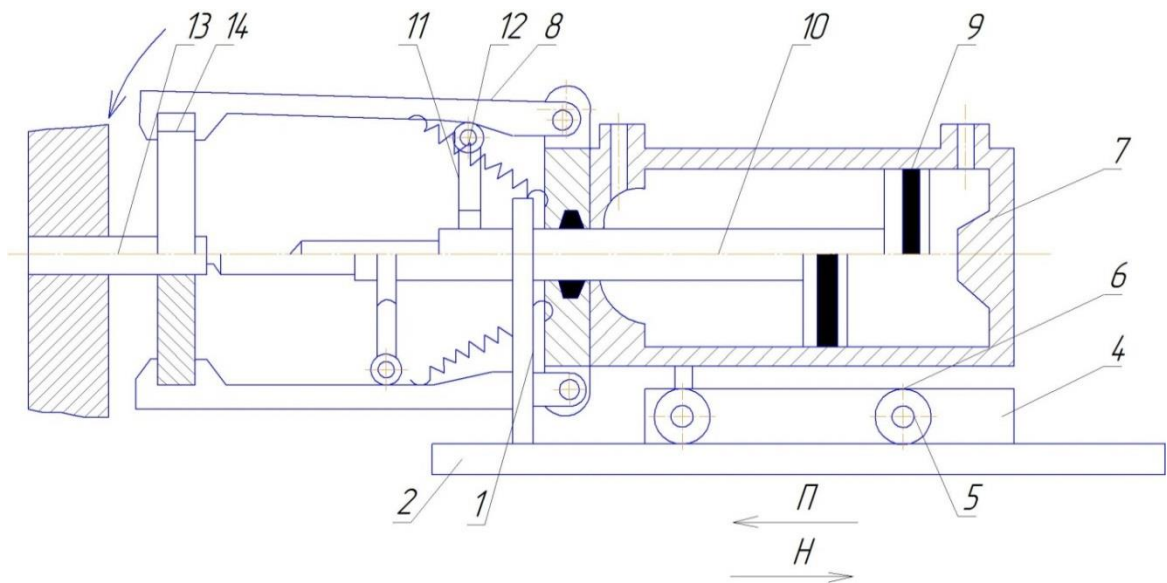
Стенд для демонтажу пресових з'єднань 1 – основа; 2 – обмежувач ходу; 3 – мікровимикач; 4 – напрямні; 7 – гідроциліндр; 8 – захоплювачі; 9 – поршень; 10 – силовий шток; 11 – траверса; 12 – переміщувальні ролики; 13 – вал; 14 – деталь, що знімається.
